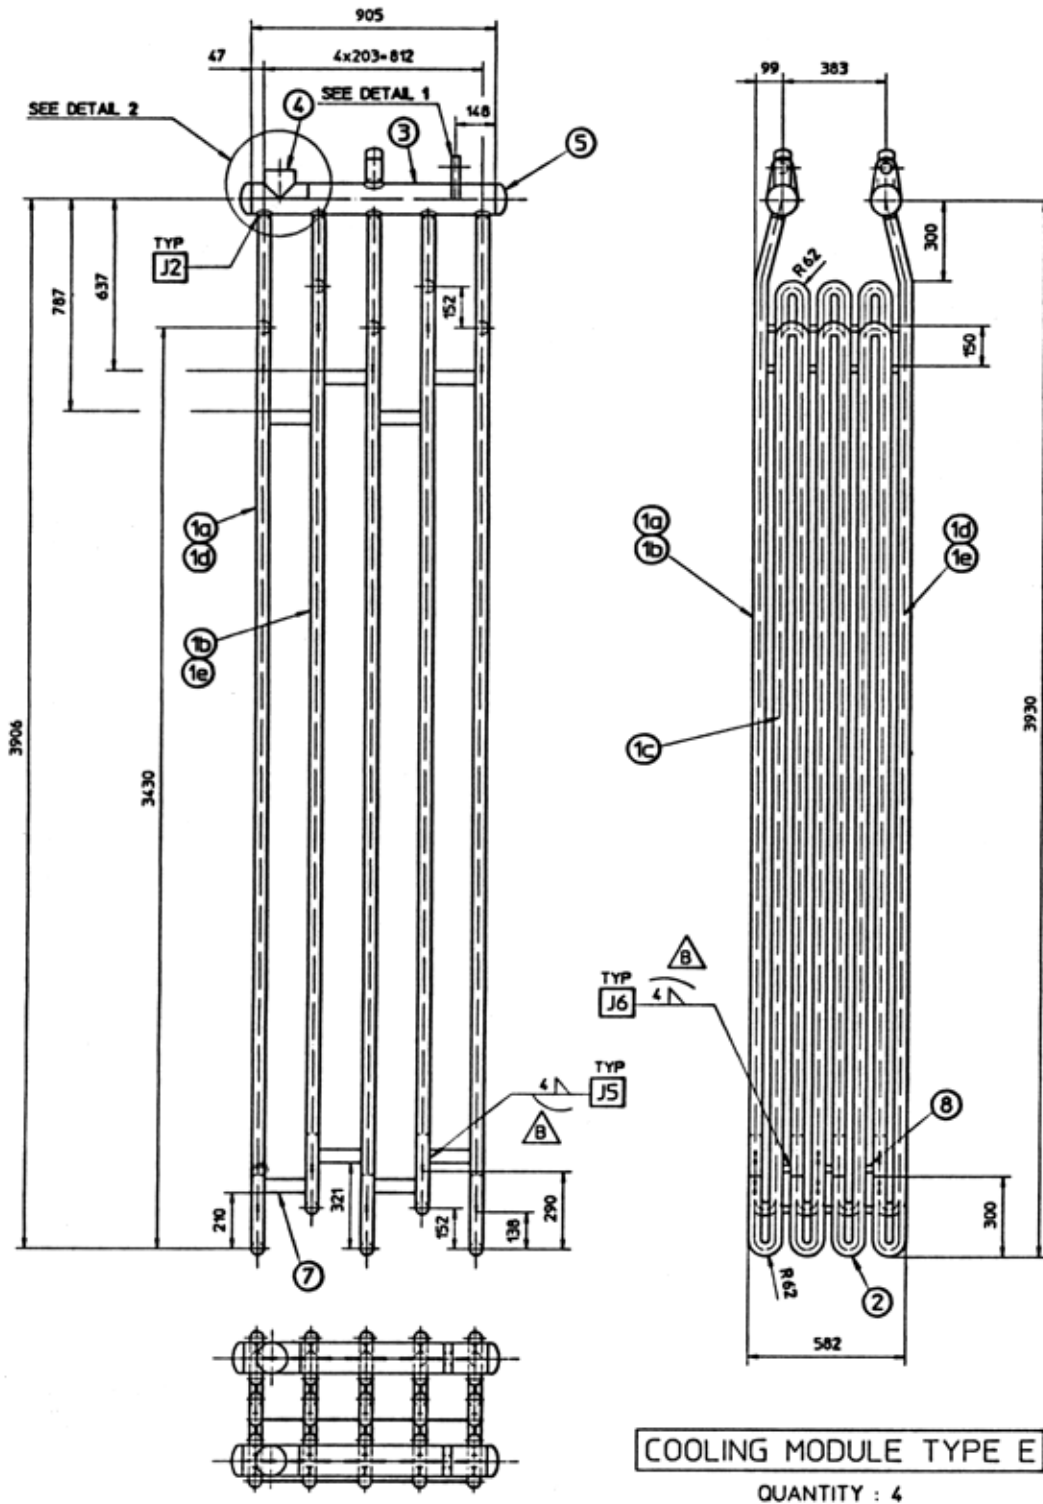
Plan d'ensemble d'un faisceau de tube d'un module de refroidissement (316L)
